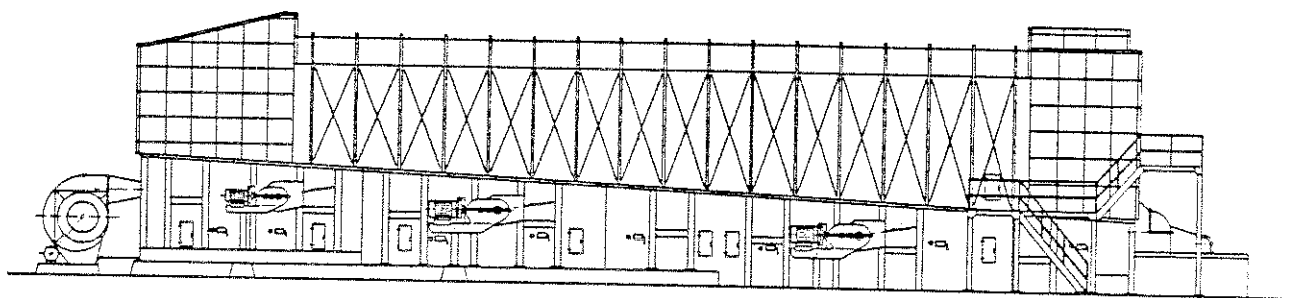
Humboldt-Wedag-Schrägrost-Klinkerkühler
